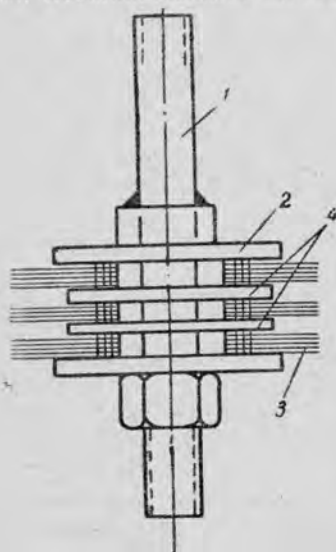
Металлическая щетка для чистки стенок обсадной трубы:
